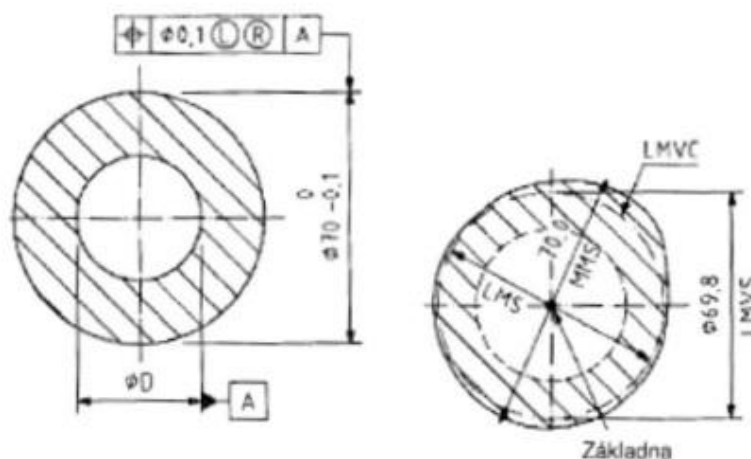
Plné využití geom. tolerance a maxima materiálu [11]
